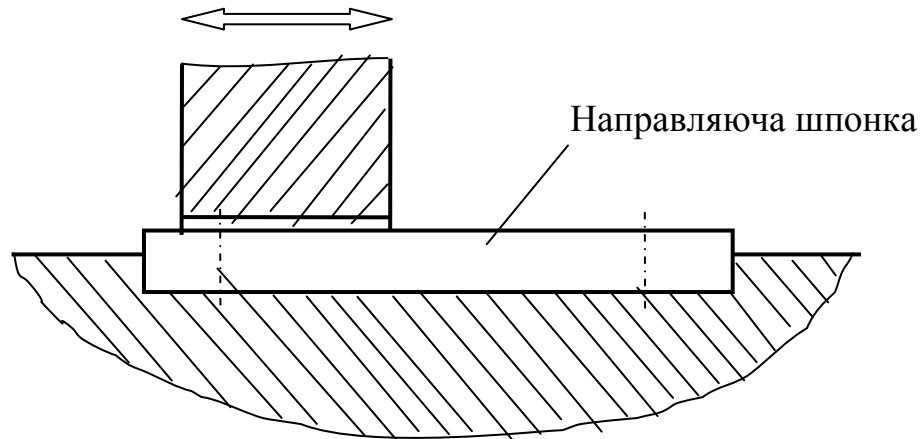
Ковзаюче шпонкове з'єднання
